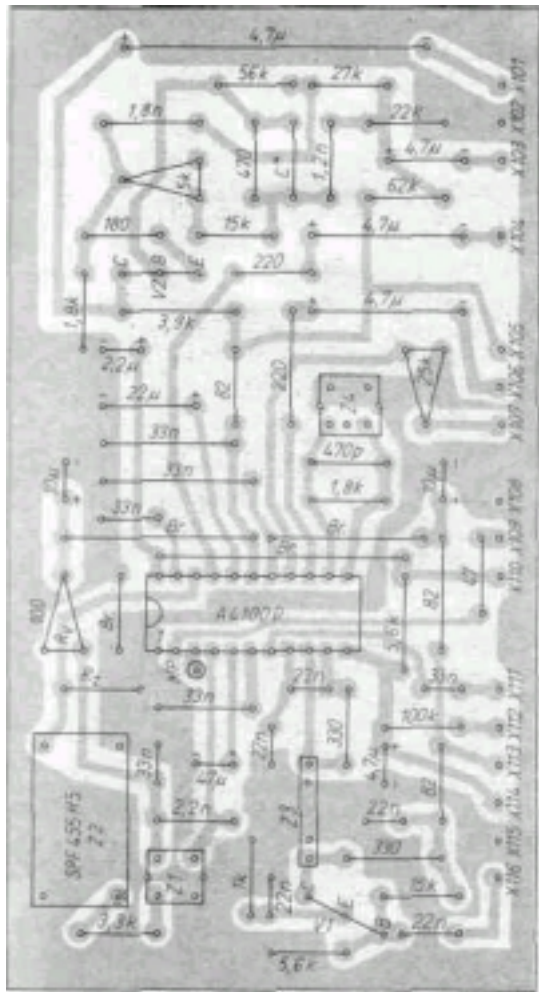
Bestückungsplan für A 1 (Br. = Drahtbrücke)
